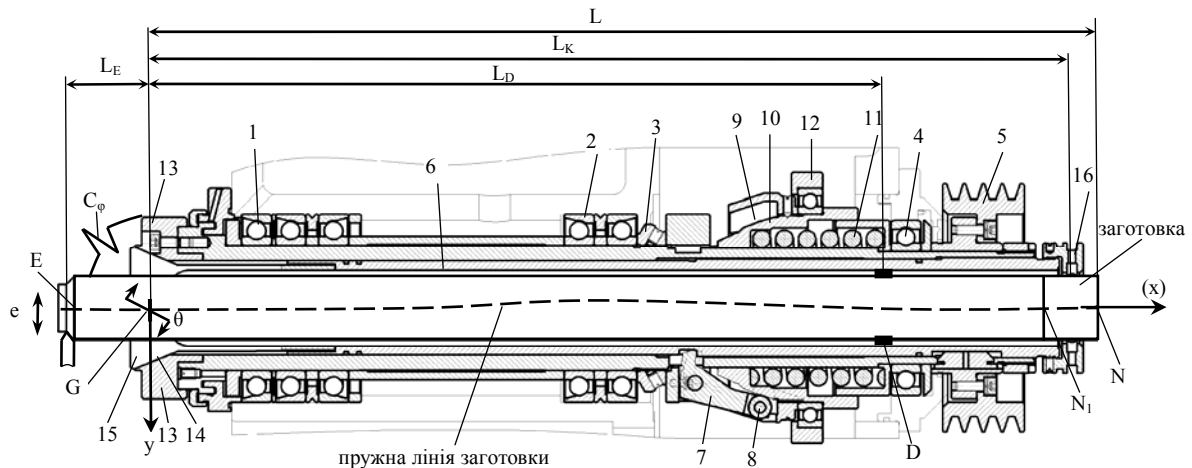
Шпиндельний вузол модуля комплексу ТАК із встановленою в патроні заготовкою
